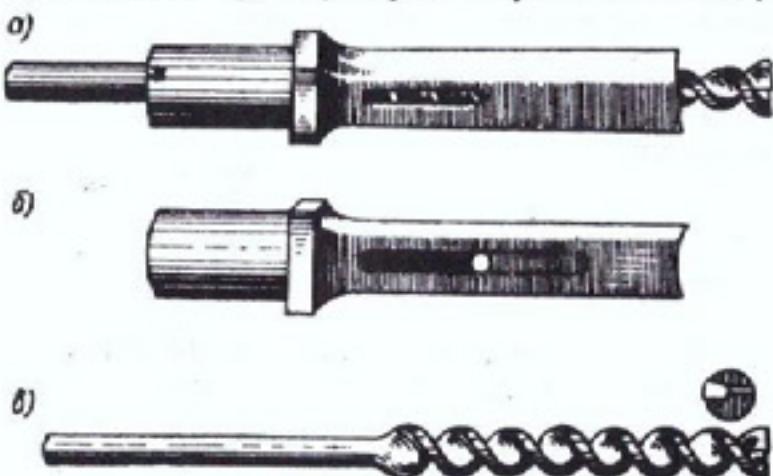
Полое долото для долбечного станка: а — общий вид долота в сборе; б — долбяк; в — сверло.
